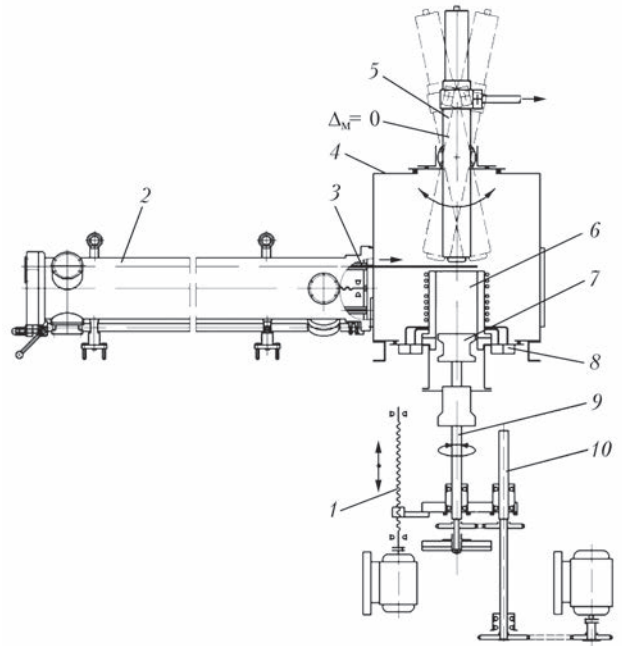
Принципова схема плазмово-індукційної установки УП-20 для вирощування монокристалів тугоплавких металів у формі тіл обертання: 1 — механізм вертикального переміщення монокристалу; 2 — бункер-касета для витратних прутків; 3 — витратний пруток; 4 — плавильна камера; 5 — плазмотрон; 6 — монокристал; 7 — піддон; 8 — водяний колектор; 9 — шток механізму вертикального переміщення монокристалу; 10 — механізм обертання монокристалу
